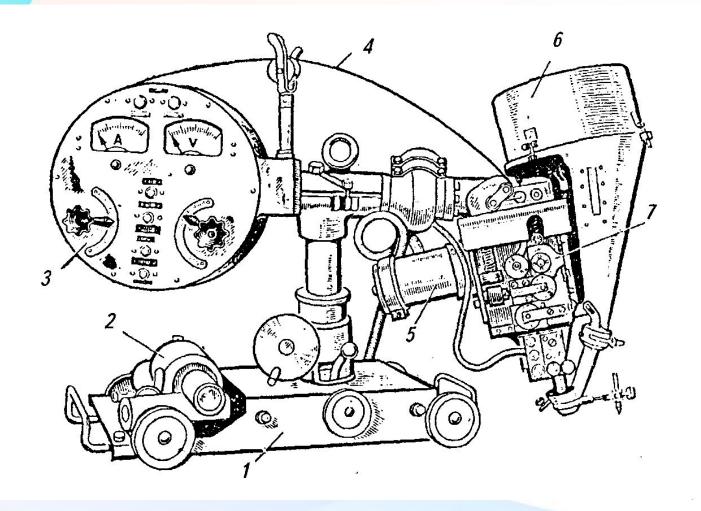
Сварочный трактор АДС-1000-2:
